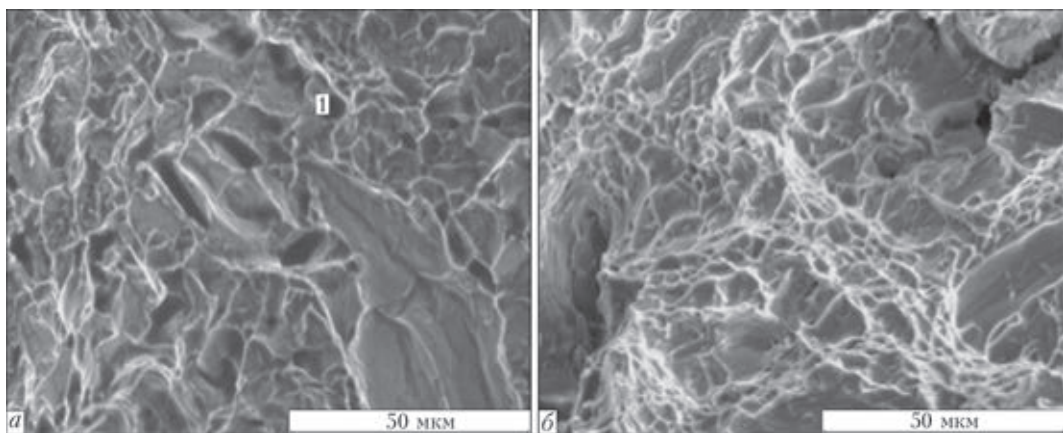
Фрактограммы поверхностей разрушений после испытаний на ударный изгиб: *a* — образца сварного соединения 1; *б* — образец 2 сварного соединения сплава технического титана BT1-0 ДШП толщиной 12 мм, упрочненного азотом (до 0,098 мас. %)
